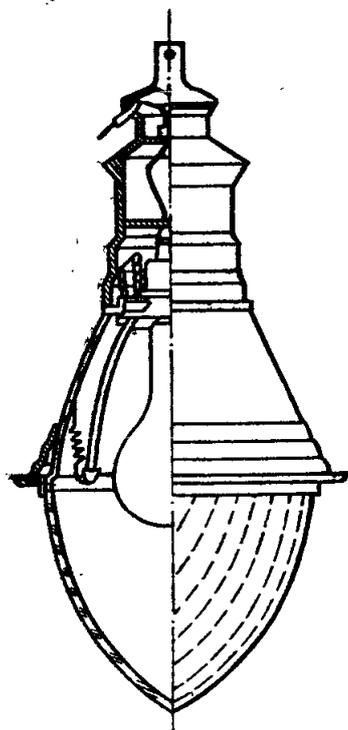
Светильник наружного освещения типа СПЗ-500
